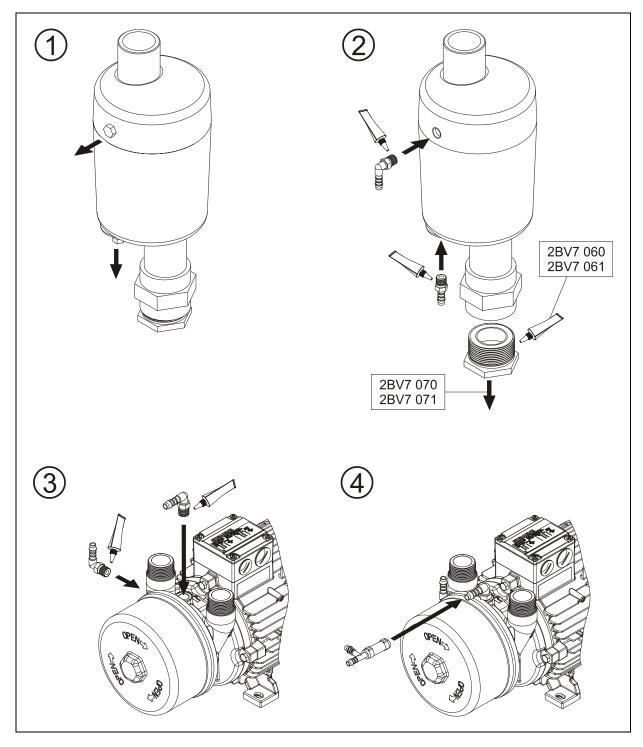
Montaggio del separatore di liquidi, parte 1 di 2
